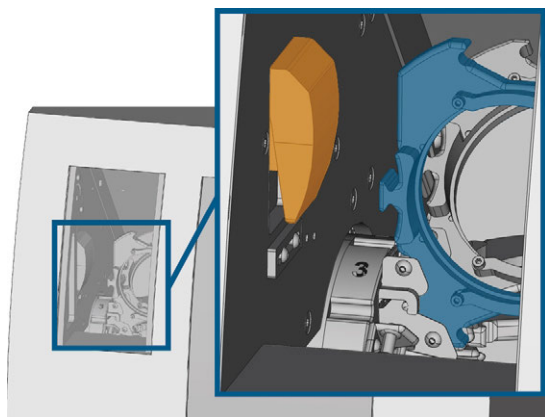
EMBOUT DE DÉTACHEMENT DU CADRE DES PIÈCES BRUTES (MARQUÉ EN ORANGE) ET CADRE DE PIÈCES BRUTES DANS LA POSITION DE CHANGEMENT (MARQUÉ EN BLEU)
